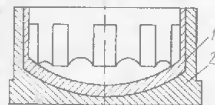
Схема конструкции осесимметричной вставки: 1 — рабочий слой; 2 — конструкционный слой
